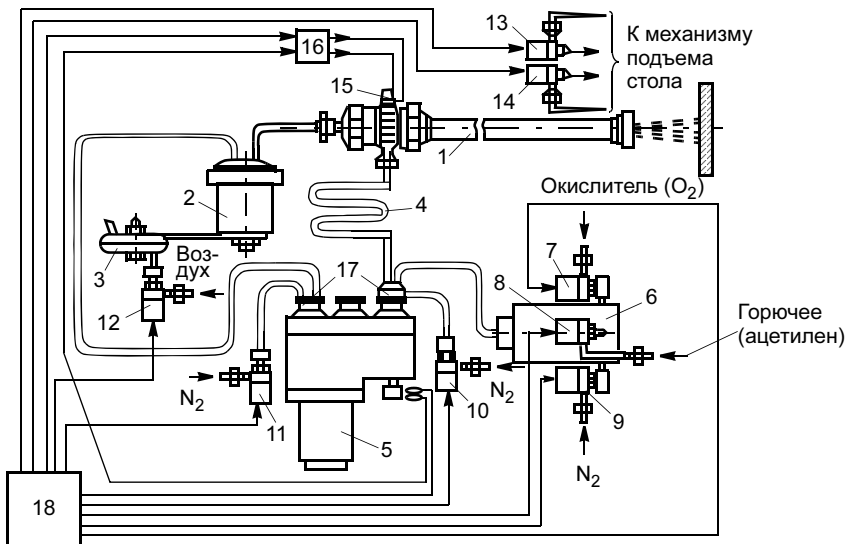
Схема АДК "Прометей": 1 — взрывная камера; 2 — дозатор порошка; 3 — пневмовибратор дозатора; 4 — буферный змеевик; 5 — блок распределения золотниковый; 6 — блок смесеприготовления; 7—14 — электропневмоклапаны; 15 — искровая свеча; 16 — генератор импульсов высокого напряжения; 17 — газораспределительные каналы; 18 — блок управления
